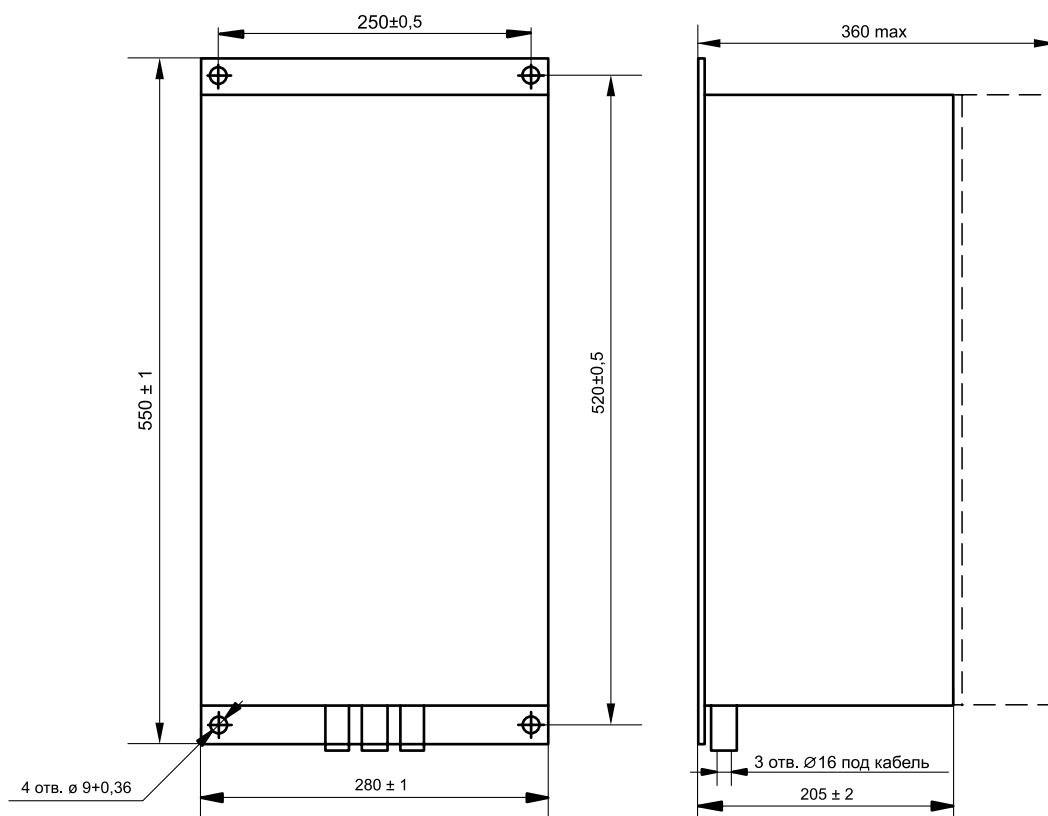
Габаритные и установочные размеры стабилизатора напряжения ИСН–М
